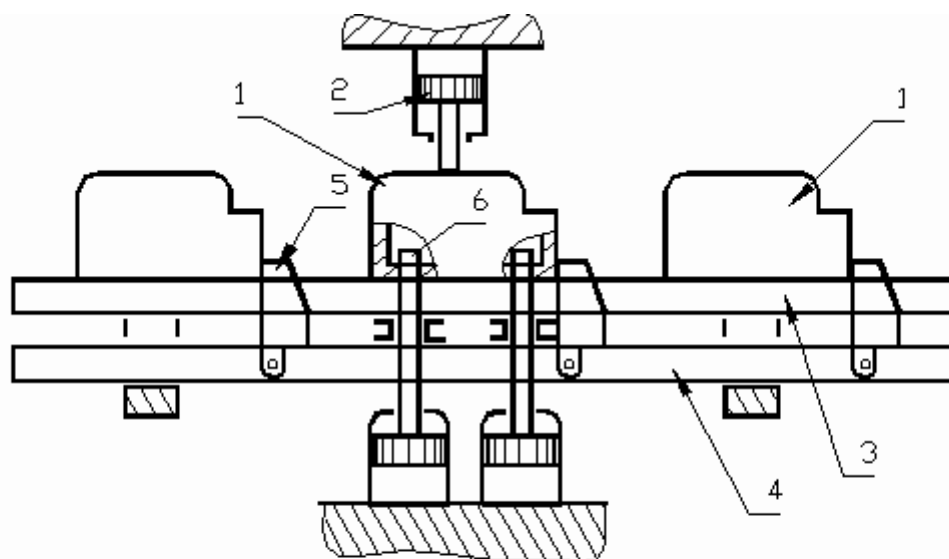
Схема полуавтоматической сборочной линии для сборки узлов с шаговым штанговым транспортом
